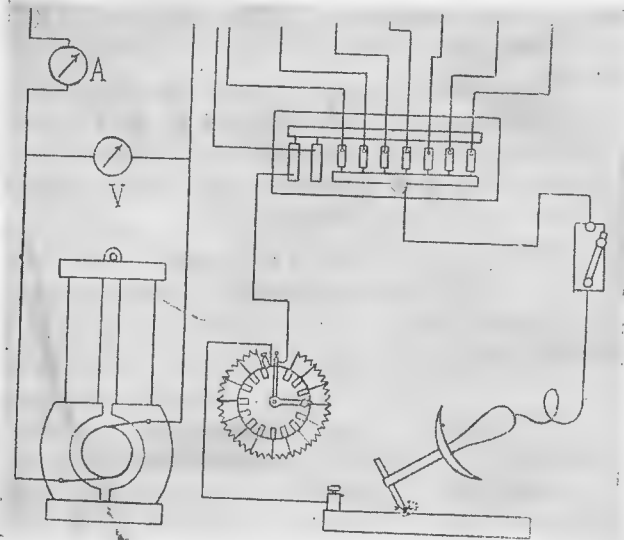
Установка для электрической сварки, изобретенной Н. Н. Бенардосом в России около 1882 г.
